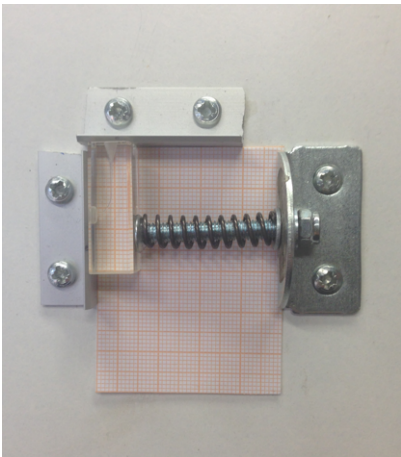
Fixierungsvorrichtung mit Millimeterpapier
